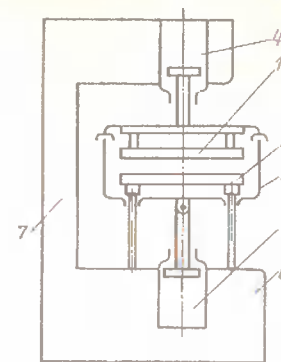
Конструктивная схема высокочастотного сварочного пресса:
